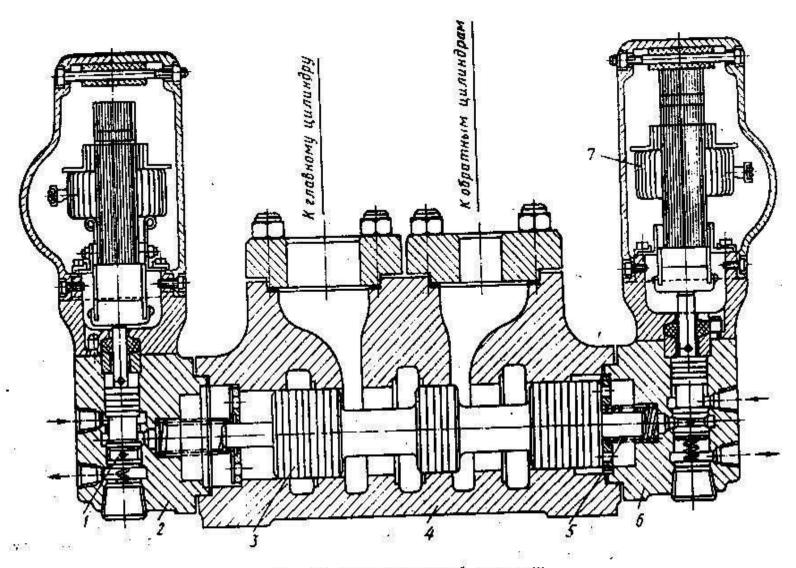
Трехпозиционный золютник: 1— золотник переключателя, 2, 6— корпус переключателей, 3— основной золотник. 4— корпус. 5— пружина, 7— электромагият
